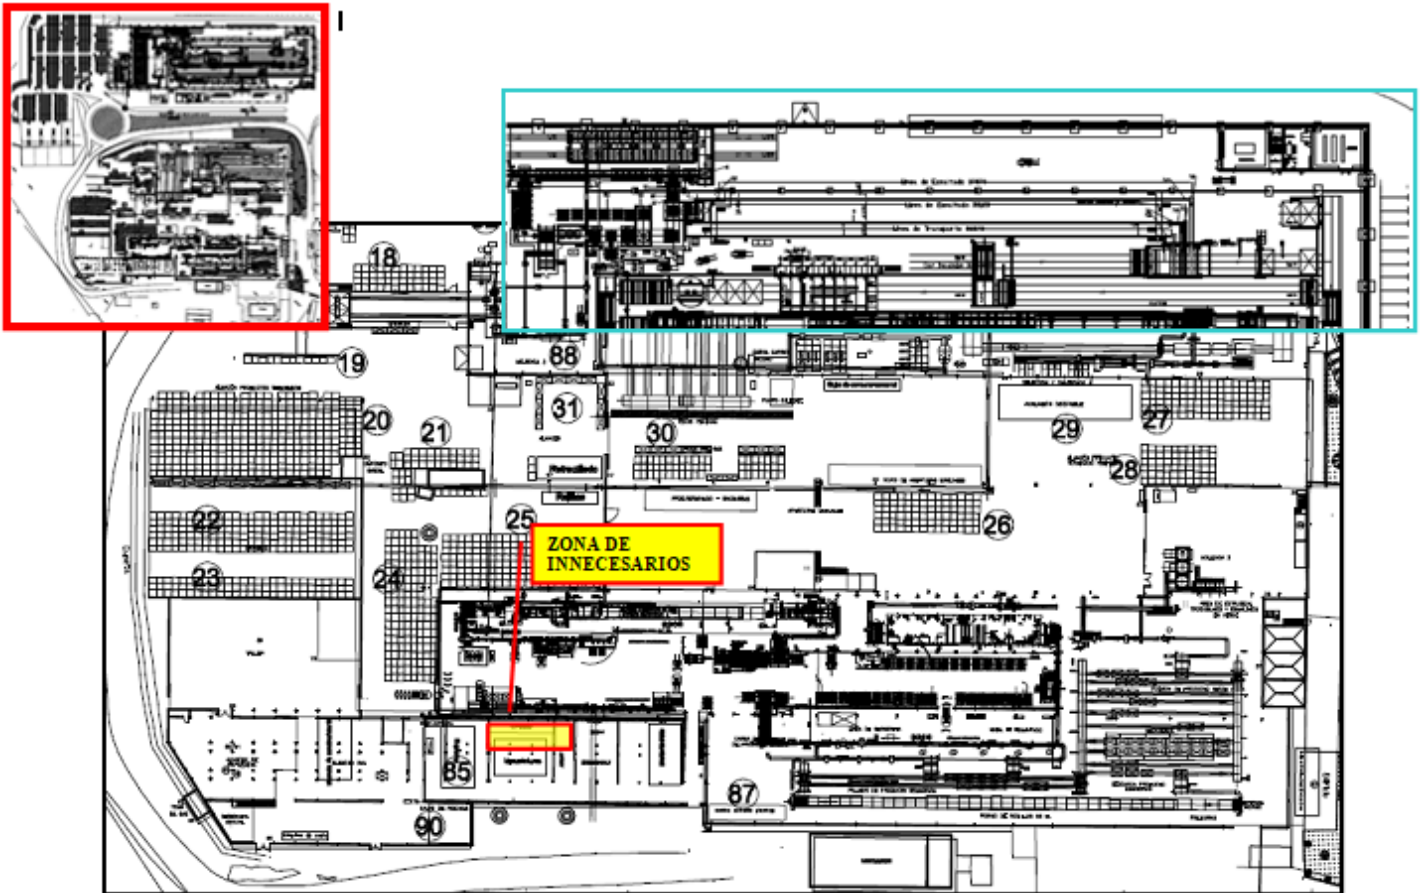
Ubicación de la zona de innecesarios 5S's en el plano.
